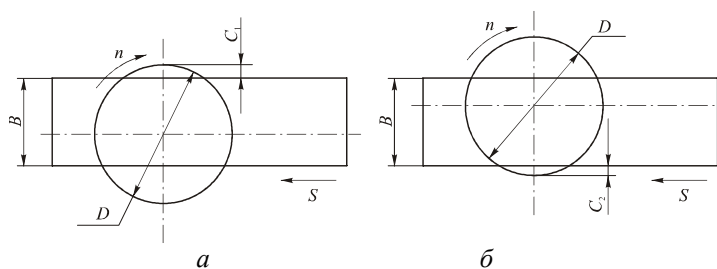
Расположение стальной заготовки при торцовом фрезеровании относительно фрезы: а – врезание зуба фрезы при $c_1 = (0,03 \dots 0,05) D$; б – выход зуба фрезы при $c_2 = 0$.
